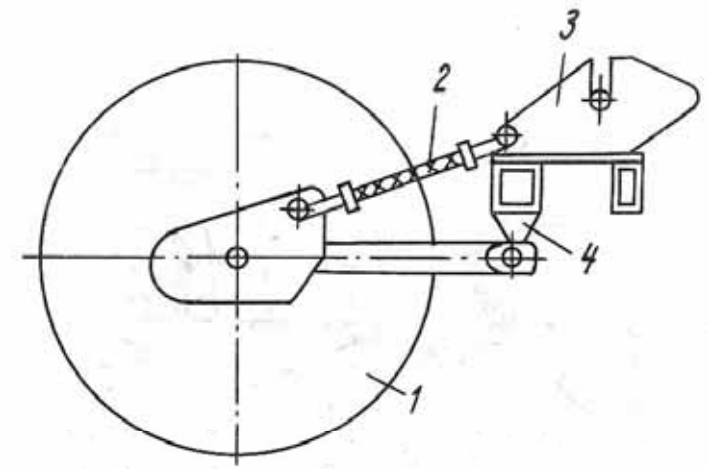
Регулировка опорно-приводного колеса: 1 - опорное колесо; 2 - тяга регулировочная; 3 - рама; 4 - косынка подвески колеса
